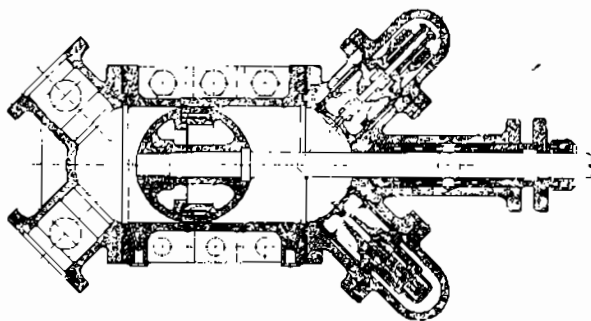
7 представляют в разрезах компрессоры трех названных систем, а именно: фиг. 5 — цилиндр аммиачного компрессора, фиг. 6 — цилиндр углекислотного компрессора и фиг. 7 — цилиндр сернистокислотного компрессора.
